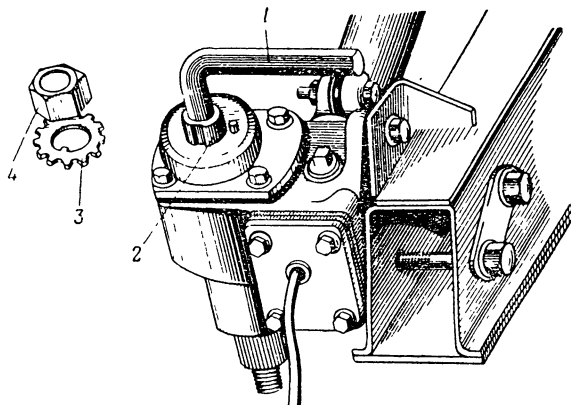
Регулировка зазора в зацеплении ролика с червяком:
